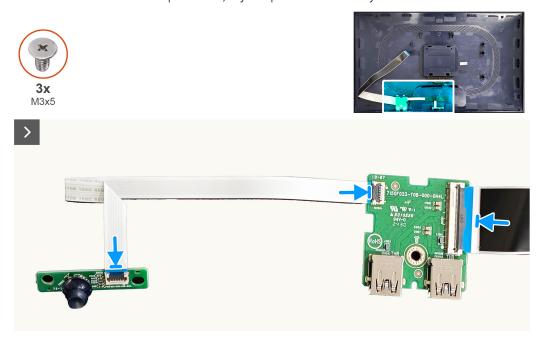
Instalar la placa de E/S y placa del botón Joystick
